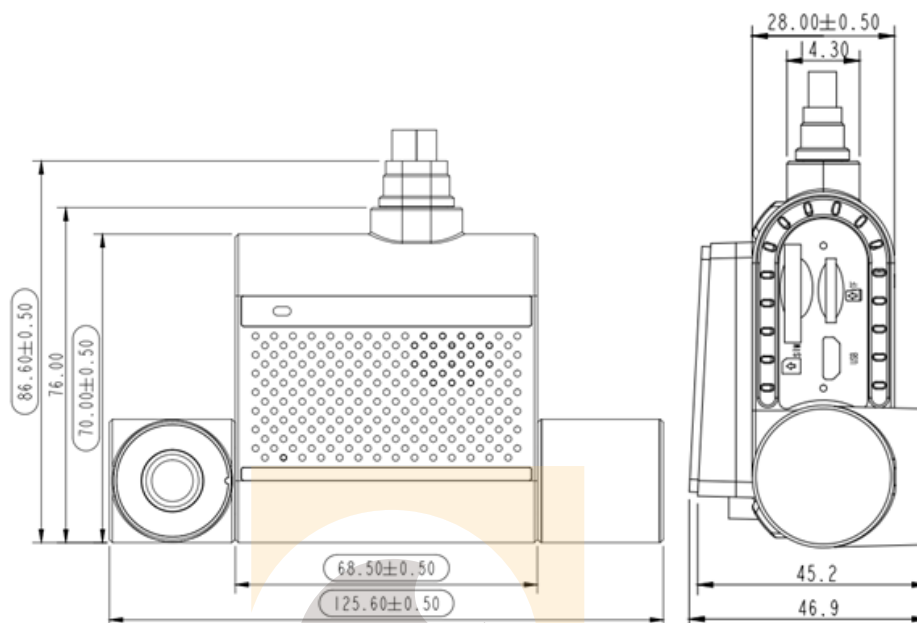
Габаритные размеры CARVIS DC-472SD
